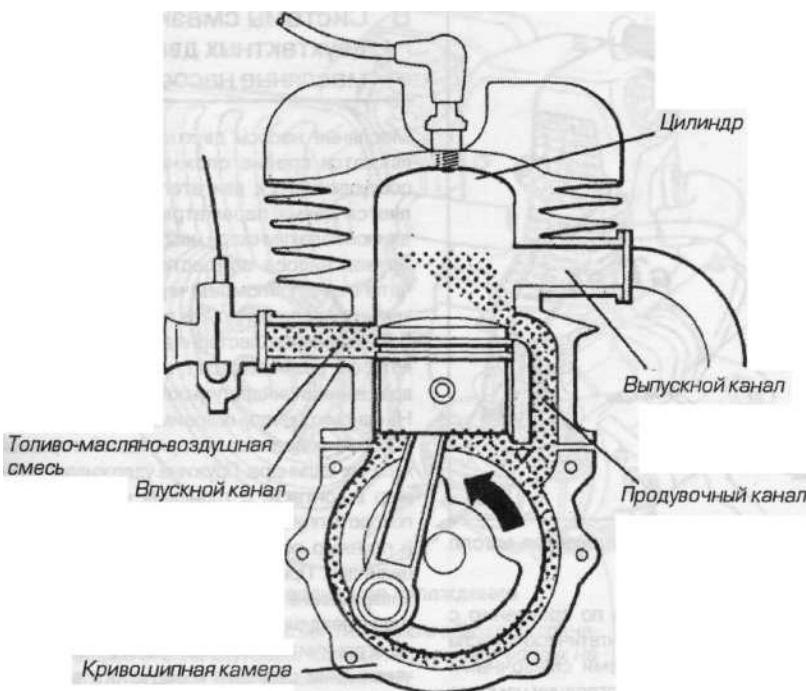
Система смазки двухтактного двигателя с предварительным смешиванием масла и топлива
